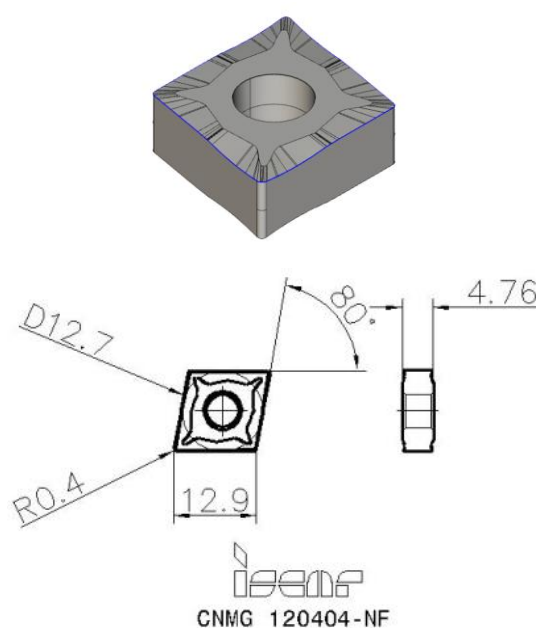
Сменная режущая твердосплавная пластина, применяемая на операции №8 при изготовлении детали «Кольцо ДА25» из сплава ХН78Т
